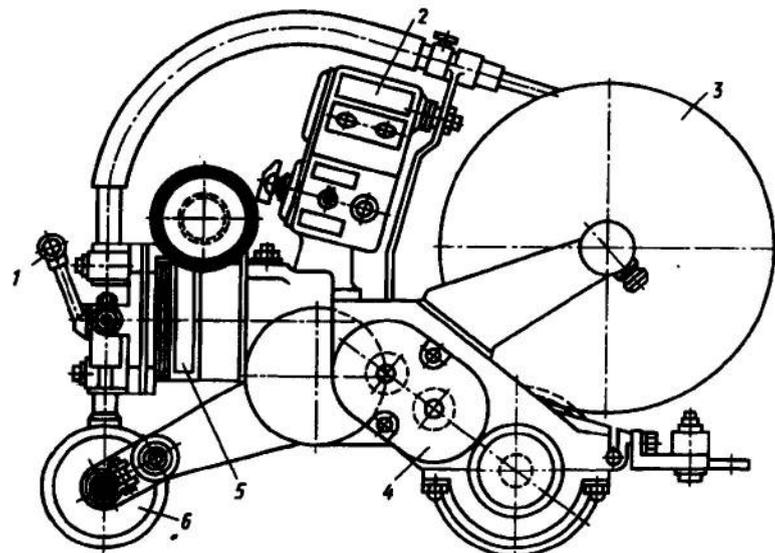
Універсальний зварювальний трактор ТС-42:
